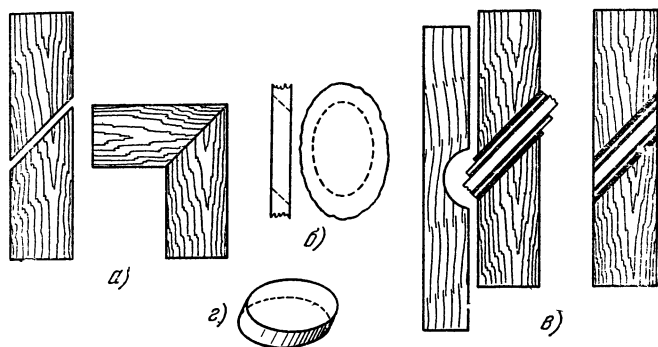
Изготовление заготовки для плоского диагонального зеркала эллиптического очертания: *а*—деревянный цилиндр, распиленный под углом в 45° ; если угол выдержан правильно, то при складывании, как показано справа, должен получиться прямой угол; *б*—кусочек зеркального стекла, обломанный щипцами; пунктиром намечены очертания будущего эллиптического зеркала (вид с поверхности и сбоку); *в*—стекло, вклеенное смолой в распил деревянного цилиндра, вместе с защитными стеклами с каждой стороны; слева—до шлифовки, справа—после шлифования лишнего стекла; *г*—законченная заготовка.
